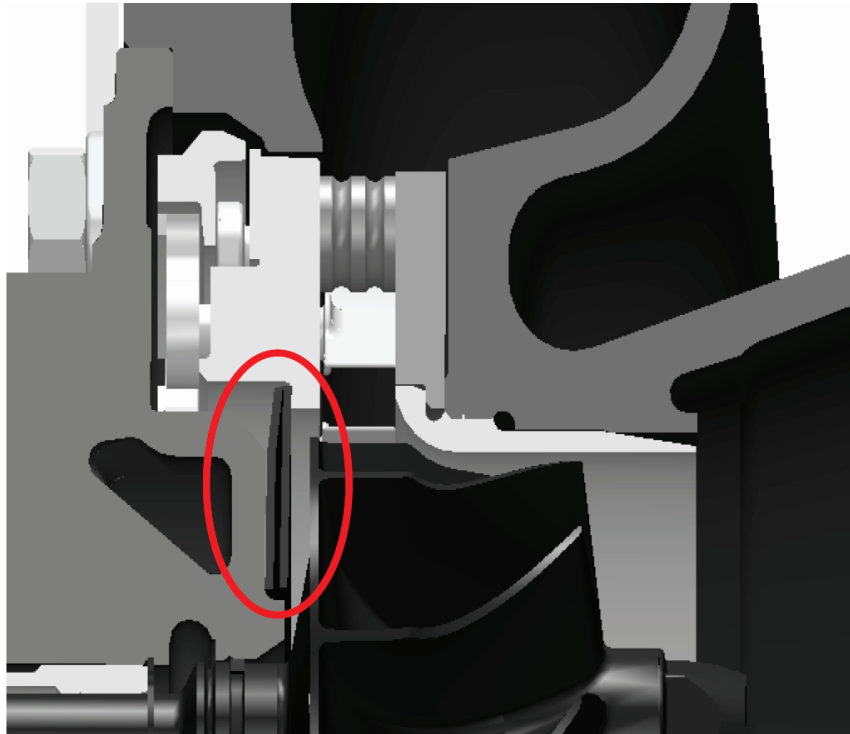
Ausschnitt Turbinengehäuse BV50G [7]
